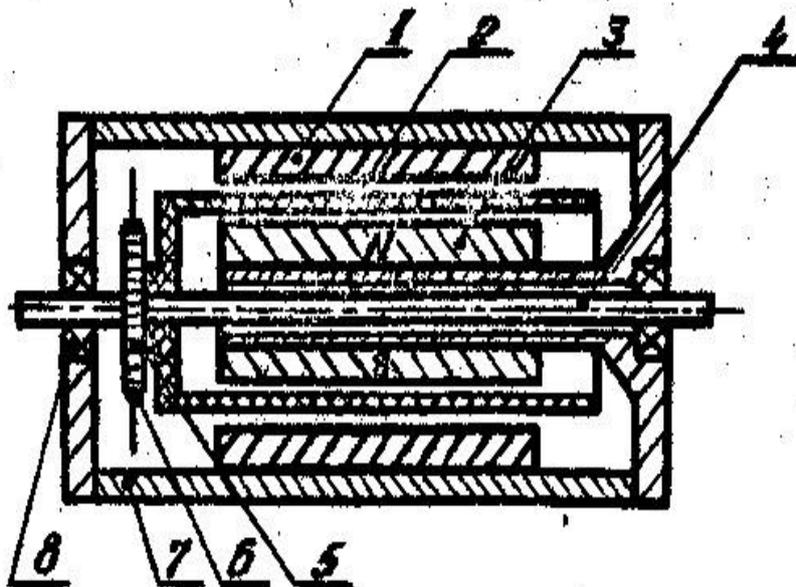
Схема конструкции двигателя постоянного тока с полым немагнитным ротором типа ДПР:
